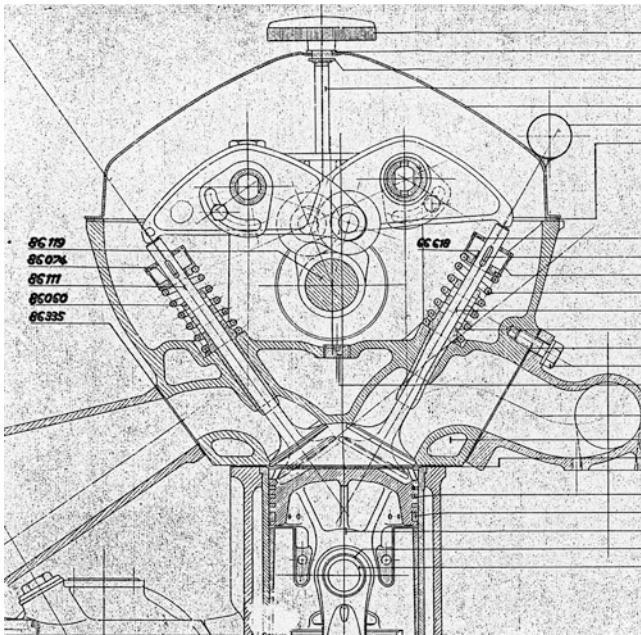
HL-35-Motor (neu): Steuerung mit Schraubenfedern als Ventilsfedern
